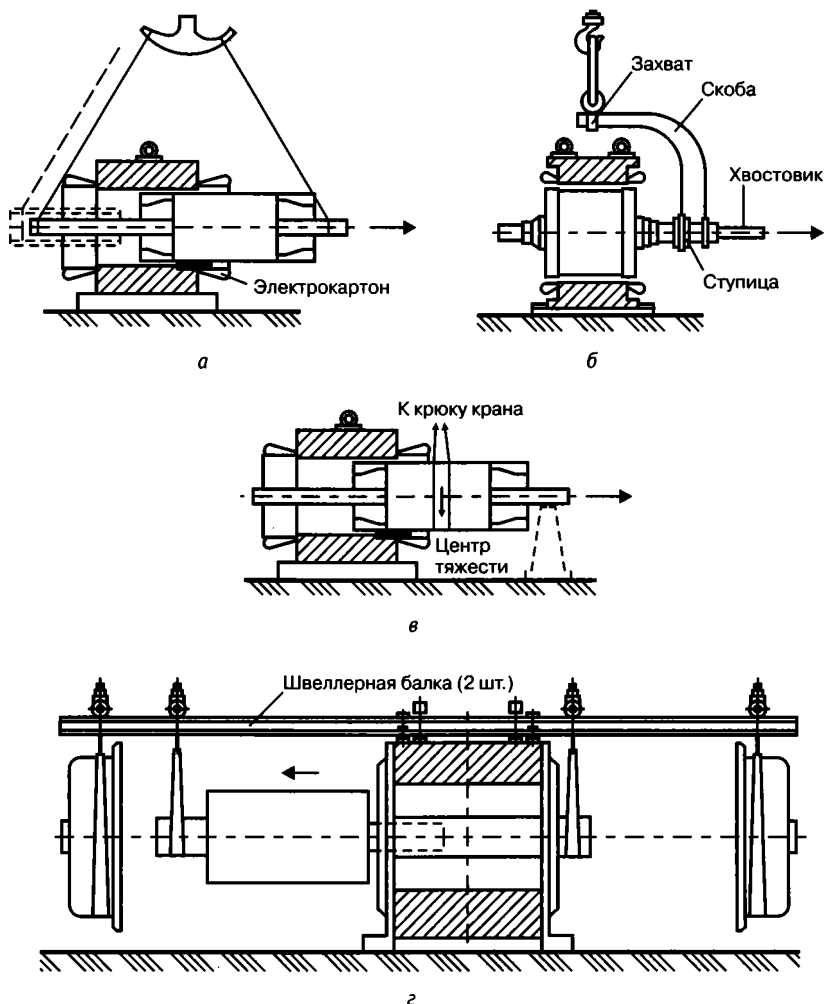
Способы вывода ротора (якоря) из статора:
